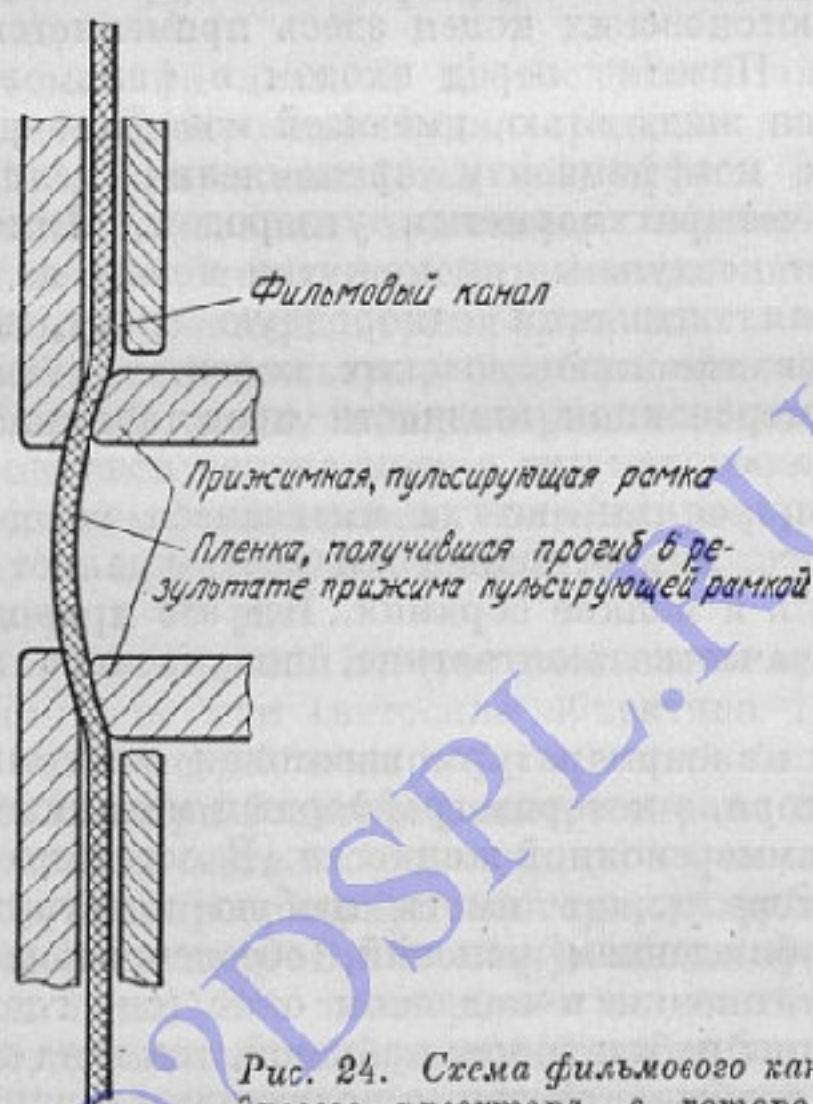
Схема фильмового канала покадрового проектора, в котором пленка прижимается рамкой, имеющей форму части поверхности шара
